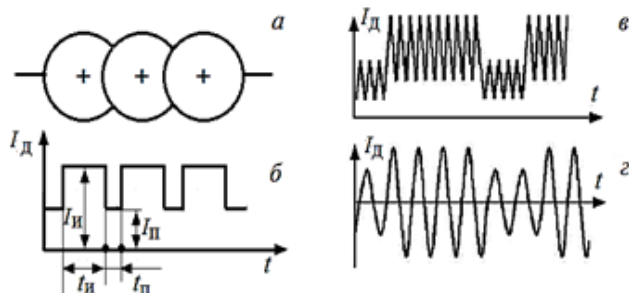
Сварка пульсирующей дугой: *а* — вид сварного шва, *б, в, г* — схематичные осциллограммы тока
